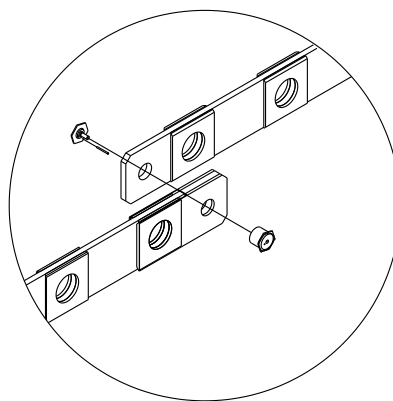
安装爬升梯 Fig. 4-12 Fitting telescoping ladder
